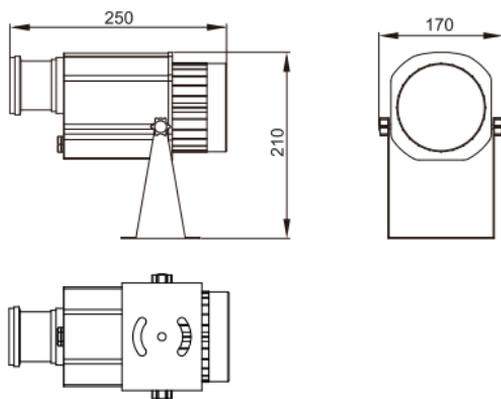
Габаритные размеры LPRU002-01-10-100-65-K03
